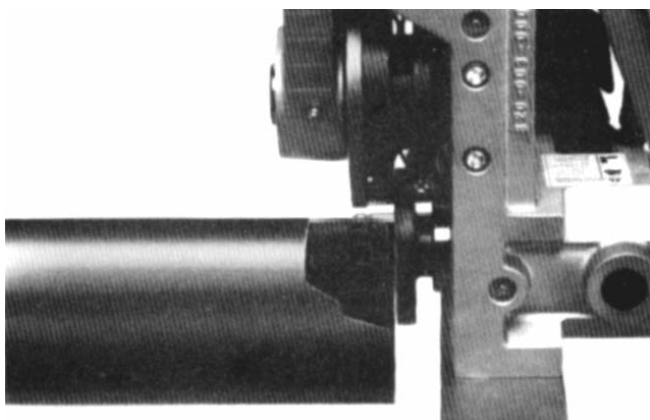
Primer plano del tubo colocado contra el reborde del rodillo de accionamiento
